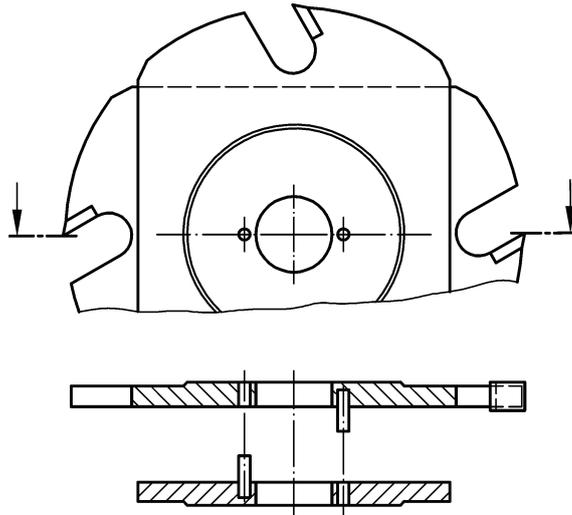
Abweiswinkel für Nichtrundform-Werkzeuge
